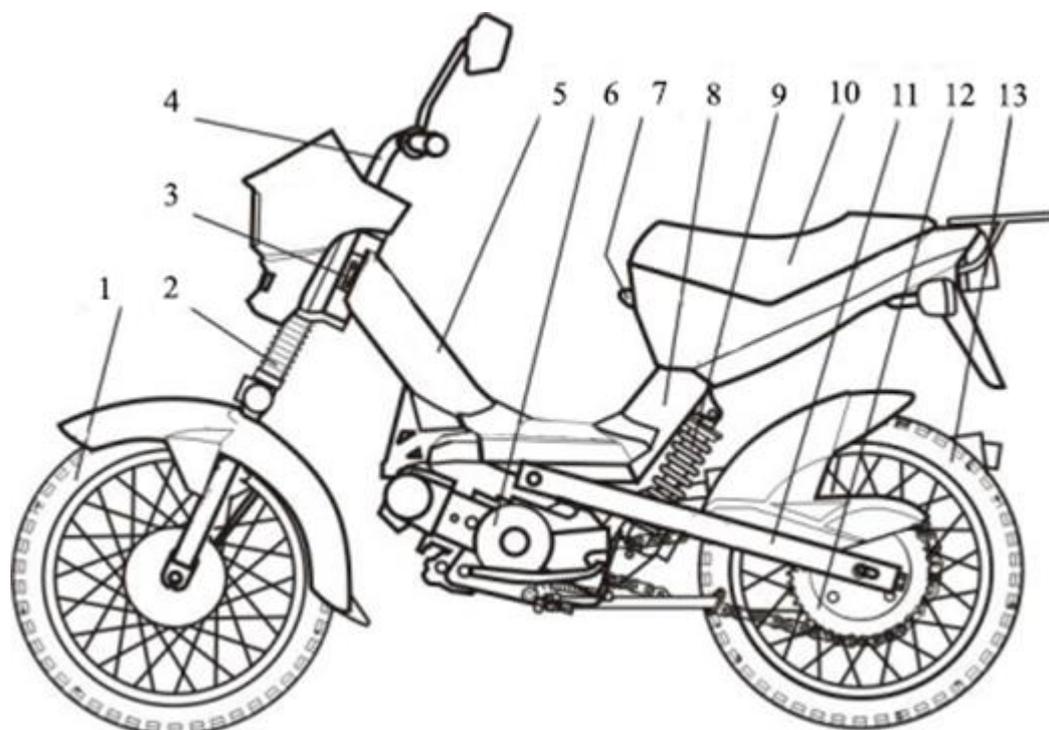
Общее устройство мопеда 1 - колесо переднее; 2 - вилка передняя; 3 – противоугонное устройство; 4 - органы управления и контроля; 5 - рама; 6 – двигатель; 7 – фиксатор седла; 8 - бак топливный; 9 - амортизатор; 10 – седло; 11 - маятник; 12 – цепная (главная) передача; 13 - колесо заднее.
